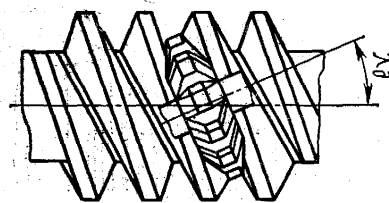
Схема нарезания цилиндрического червяка дисковой фрезой
